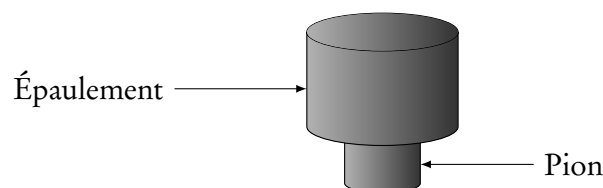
Outil de soudage par friction malaxage.
